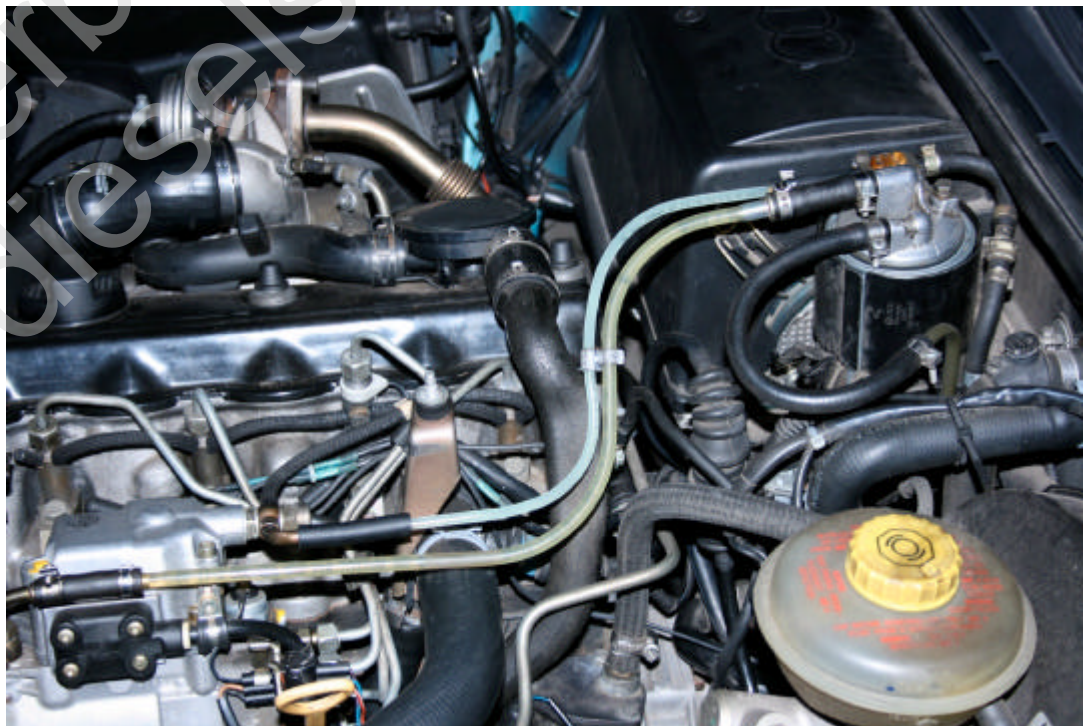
Eingebaute Rücklaufleitung (hellere Leitung) nach Formen, Kürzen, und Wiederaufbau des pumpenseitigen Anschlusses
